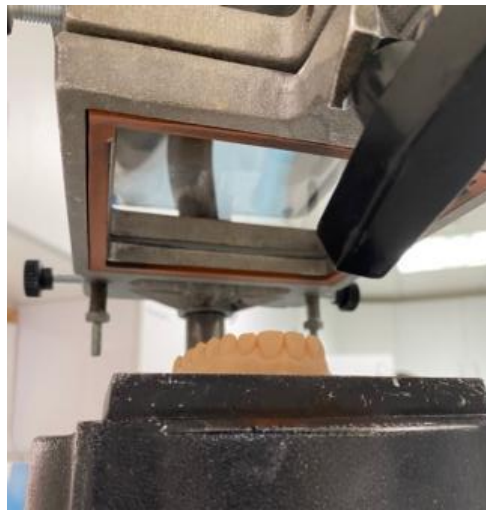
Máquina *DENTAFLUX-The thermoforming machine* com o plástico a aquecer na estrutura da máquina.
